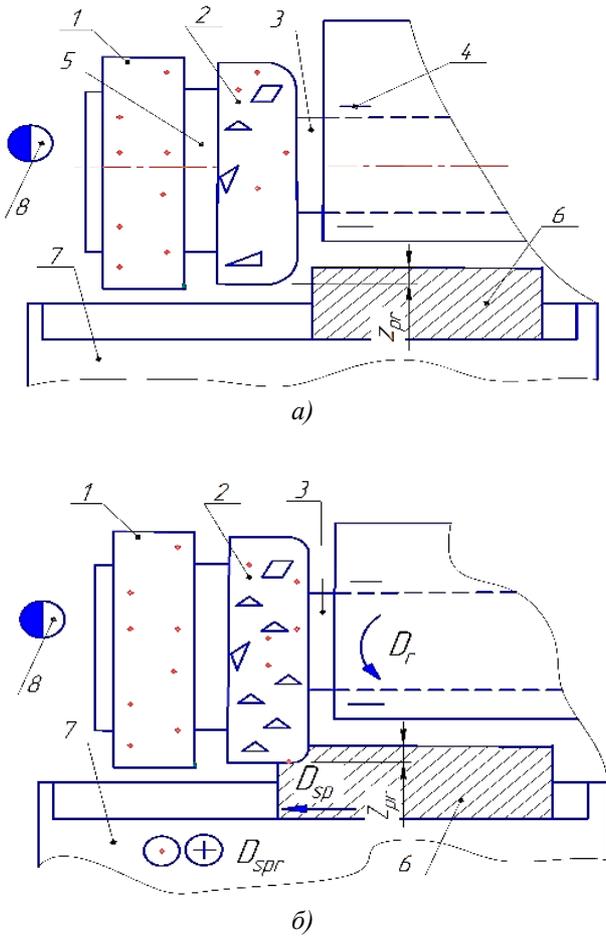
Расположение заготовки относительно шлифовальных кругов перед обработкой (а) и начало шлифования крупнозернистым кругом (б)
